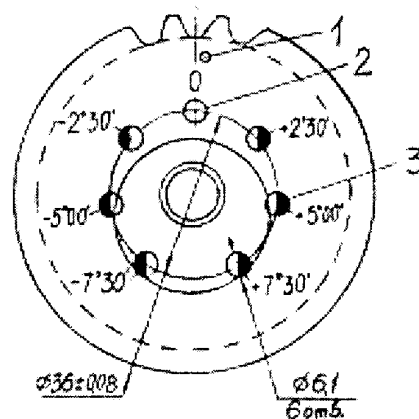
Звездочка распределительного вала с дополнительными отверстиями:
